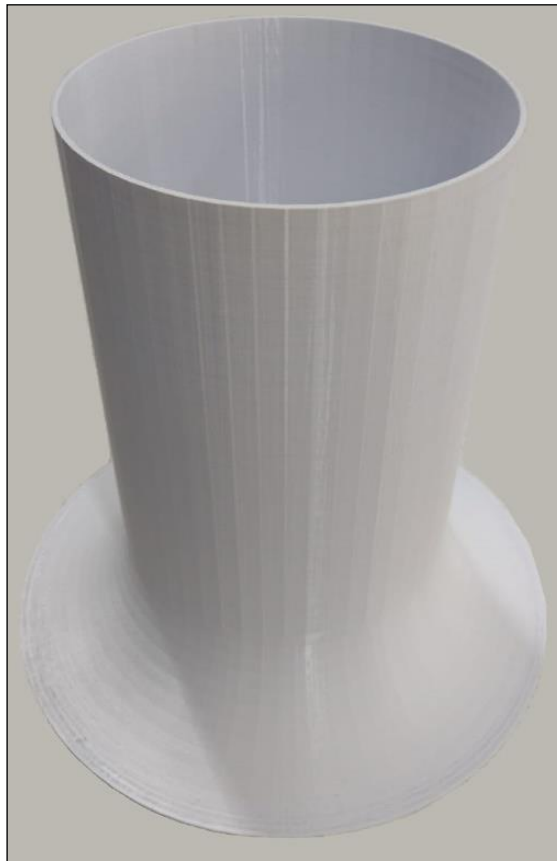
Perfil acampanado de ácido poliláctico (PLA)
